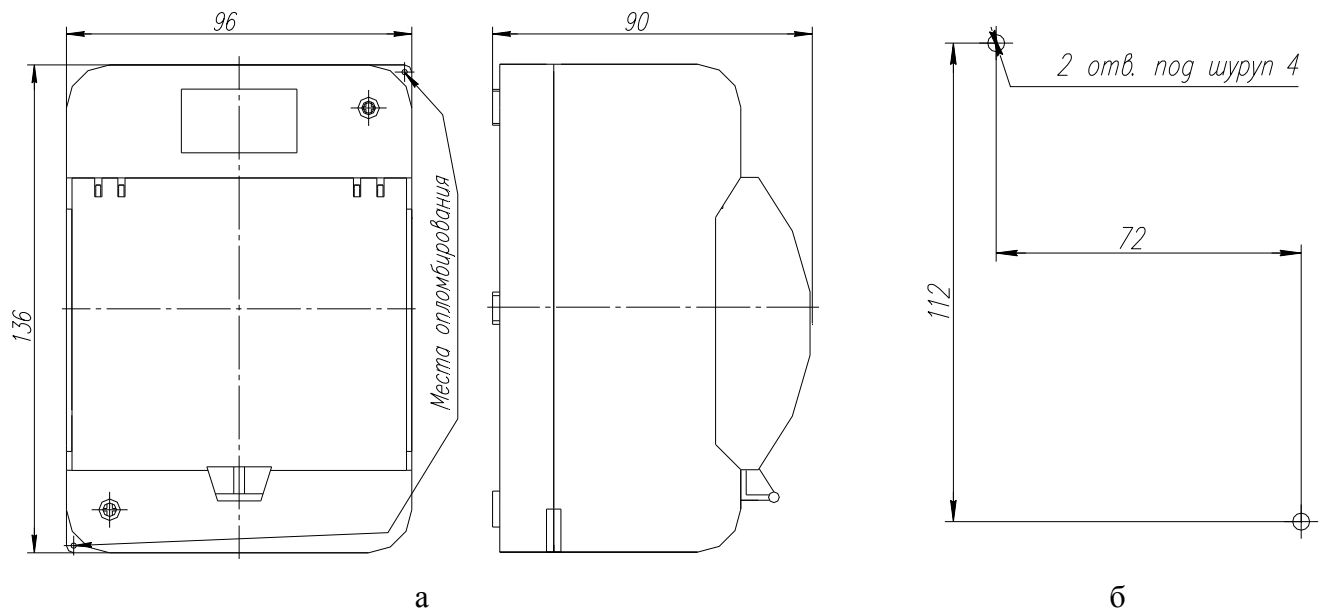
Внешний вид и габаритные размеры (а), установочные размеры (б) блока, размеры в мм.
